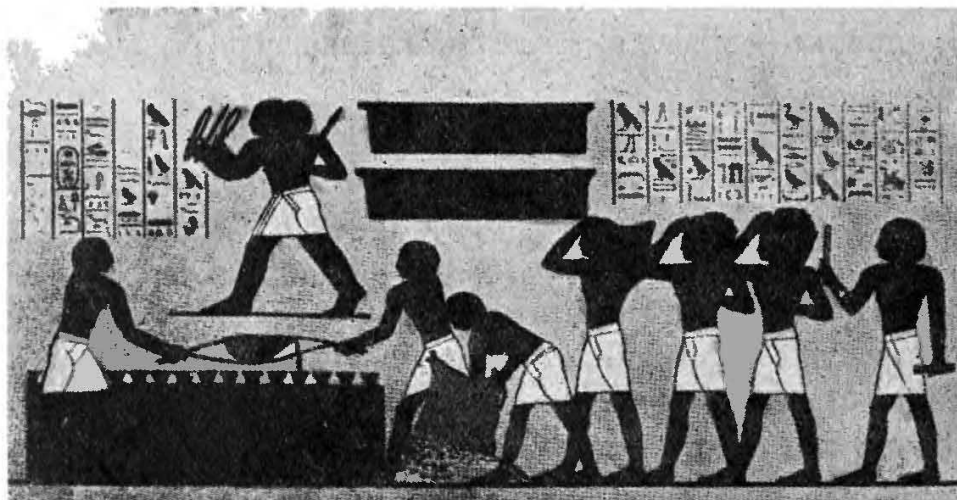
Отливка бронзовых дверей храма в Карнаке. Двое мастеров льют расплавленный металл из тигля в форму; наверху рабочее с инструментами, справа рабы с углем и болванками металла, за ними надсмотрщик.
